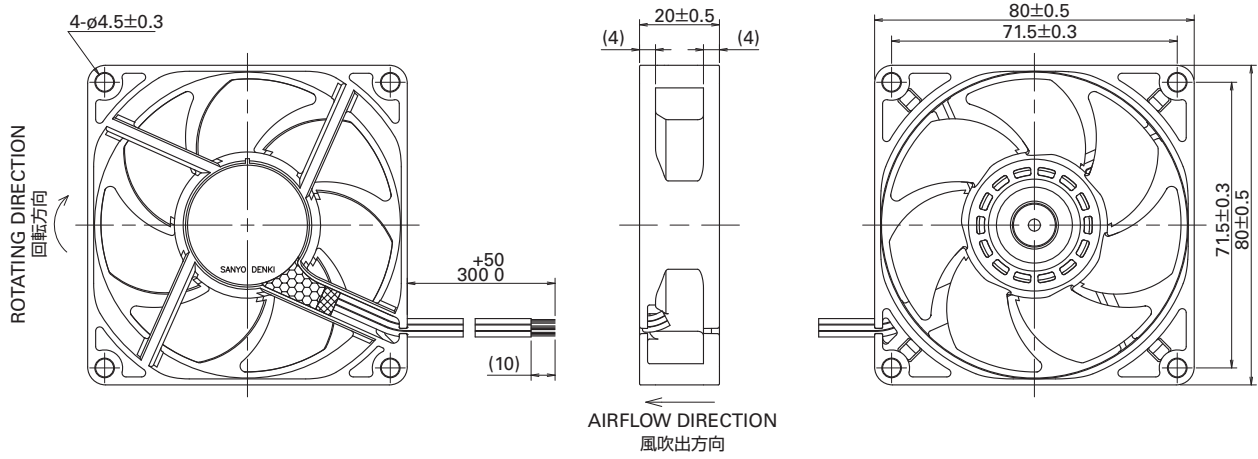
「San Ace 80WF」寸法緒元 (単位: mm)
